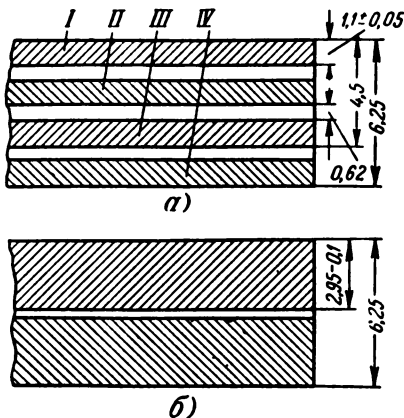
Основные размеры магнитной ленты и звуковых дорожек.
